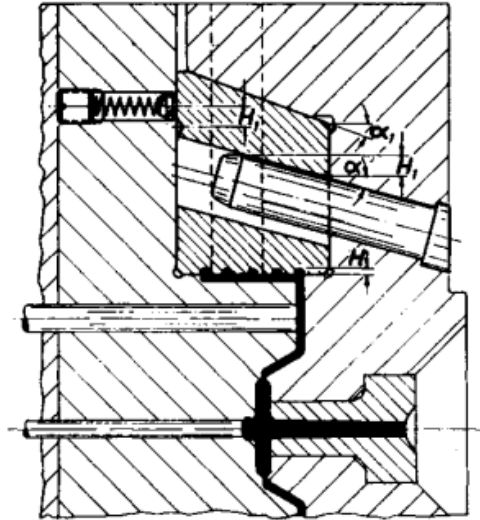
Retorno de las correderas. Fuente: How to make injection molds [7].
